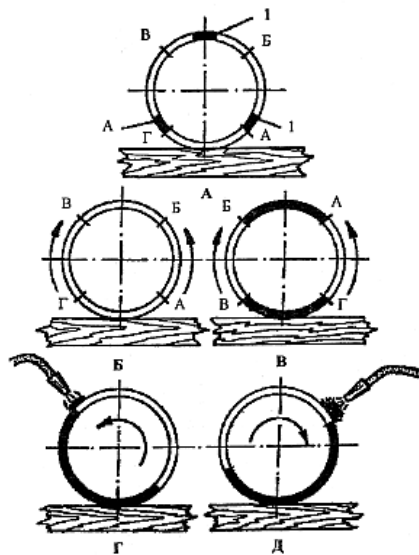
Сварка поворотных стыков: А-размещение прихваток (1); Б-выполнение первого слоя сварки на участках А-Б, Г-В; В-поворот стыка и сварка на участках Г-А; В-Б; Г-второй слой сварочного шва; Д-третий слой сварочного шва;
